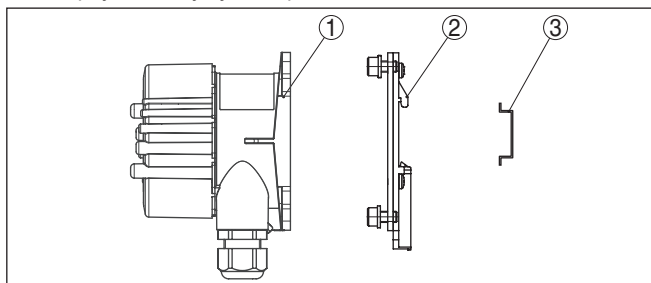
VEGADIS 81 с корпусом из алюминия или нержавеющей стали, для монтажа на несущей рейке
